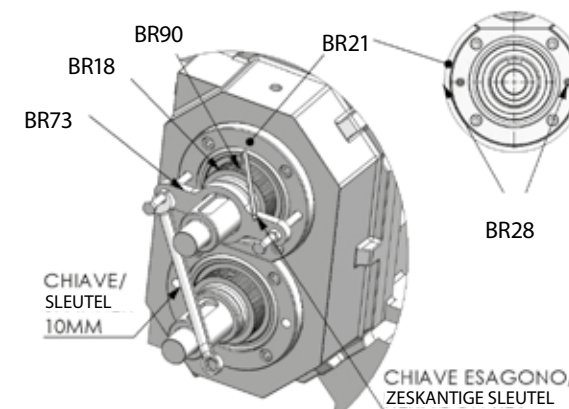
Montage mechanische dichtingen (fase 2).
